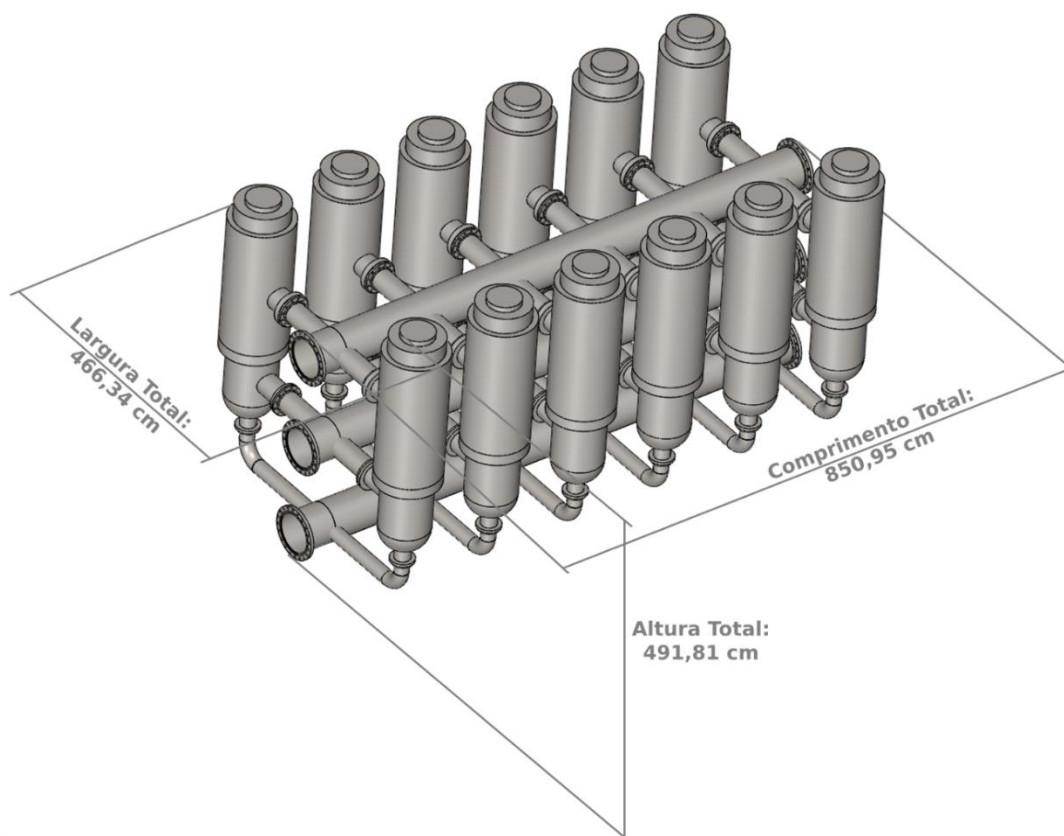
Construção 3D do *skid* individual da planta de módulos fibra oca
